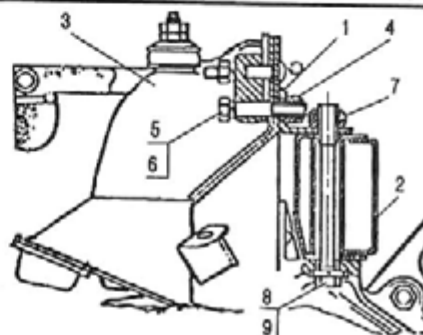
Крепление подвески к лонжерону рамы: 1 - кронштейн; 2 - лонжерон; 3 - подвеска; 4 - планка горизонтального крепления; 5 - болт; 6 - шайба; 7 - планка вертикального крепления; 8 - болт; 9 - шайба
